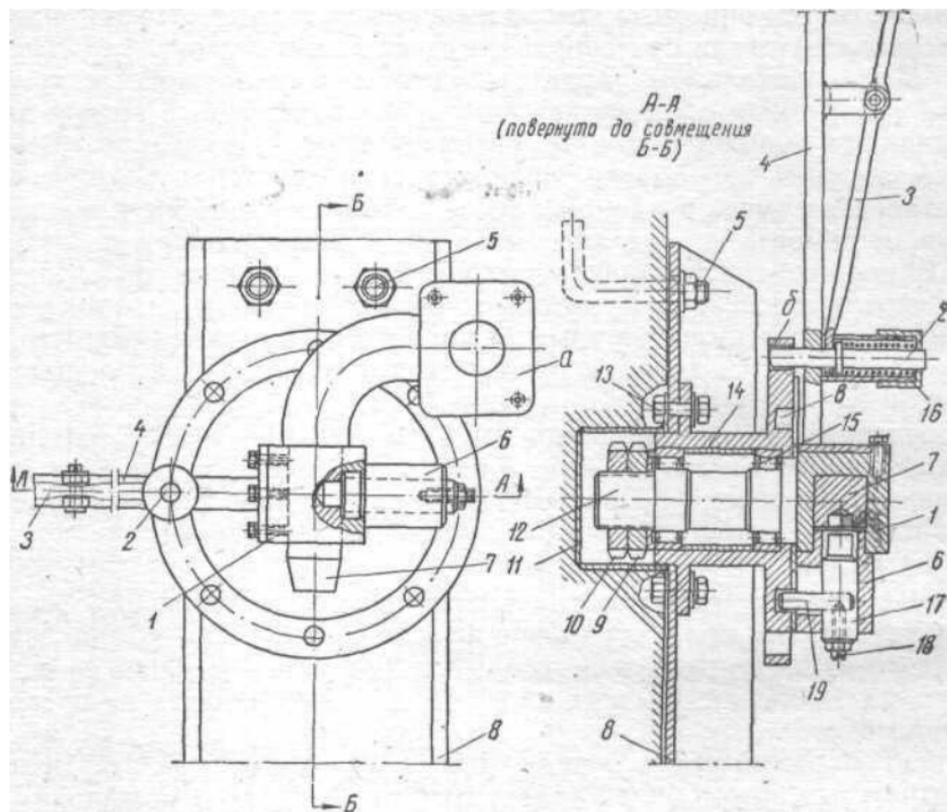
Стационарный стенд для разборки и сборки двигателя
